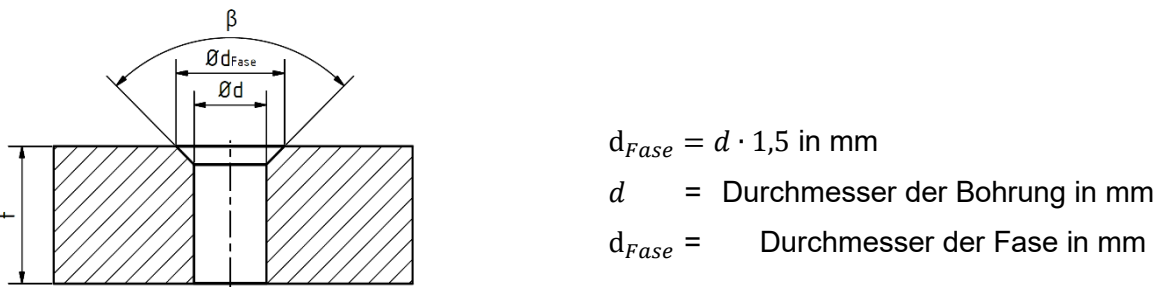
Bohrung von Schmid Schrauben mit Senkkopf in Metallbauteilen
